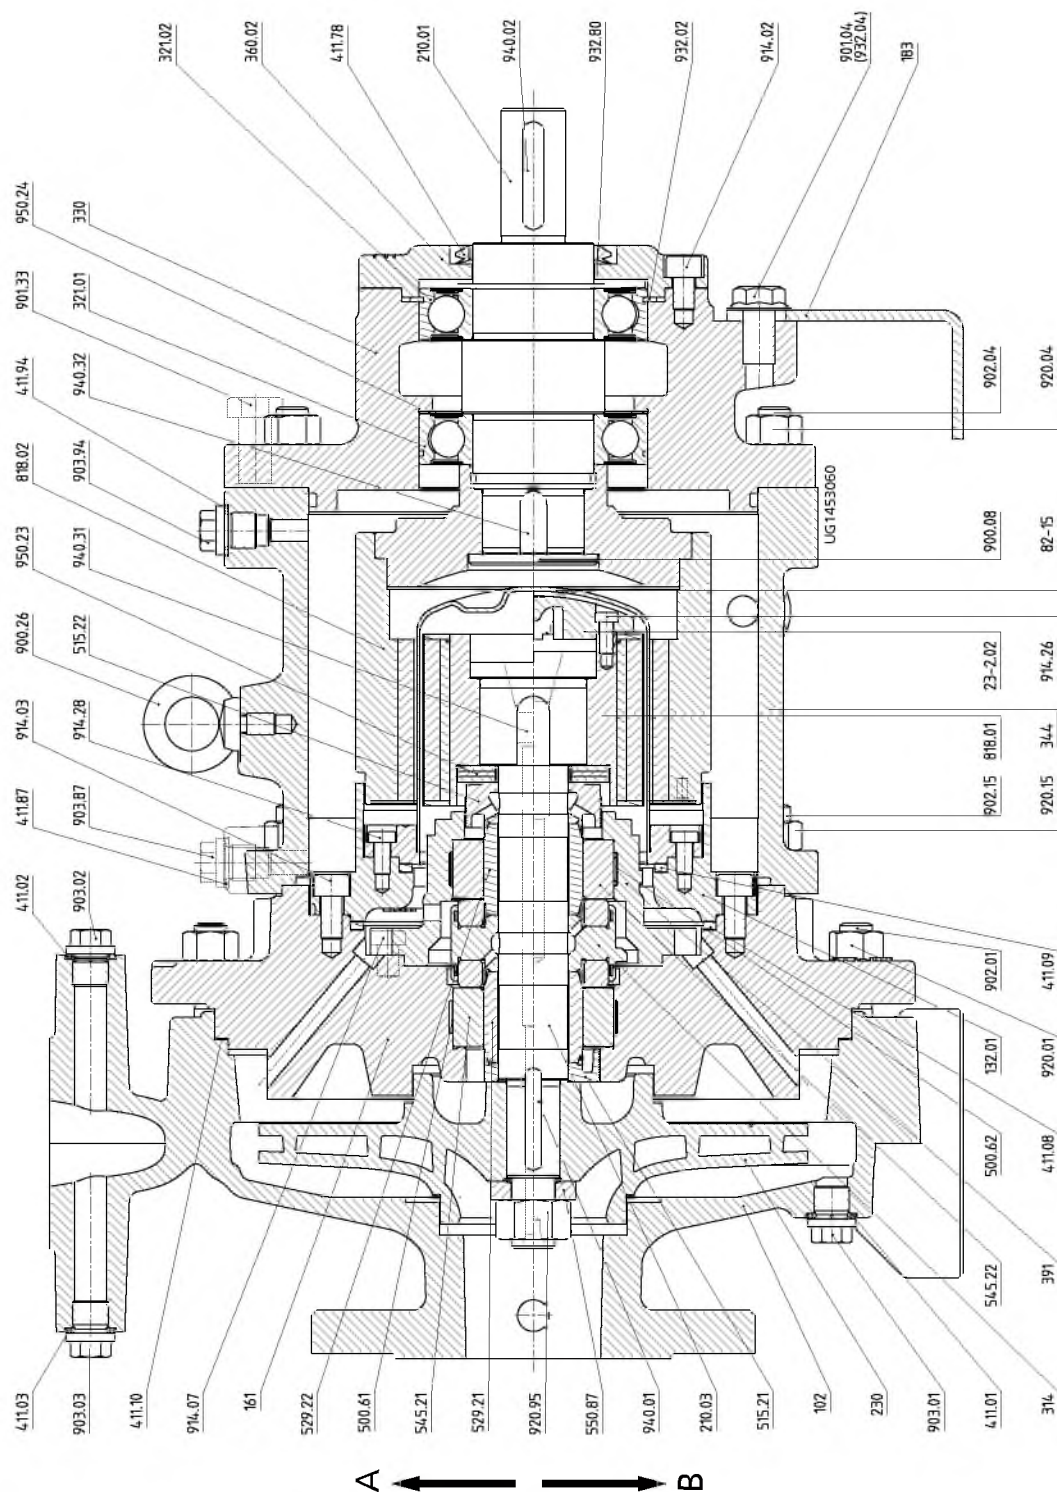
Сборочный чертеж — исполнение с привинчиваемой крышкой с проставком
